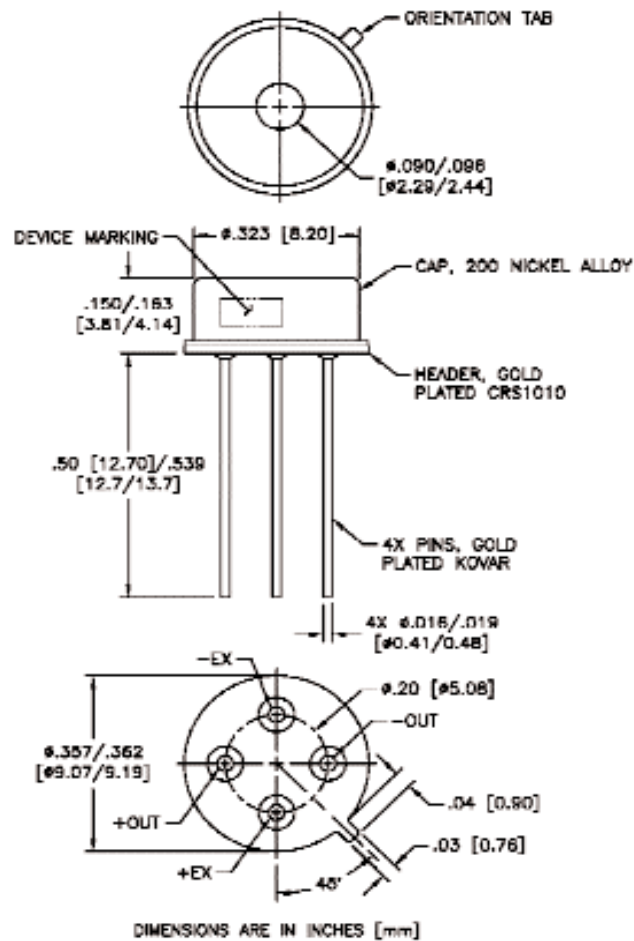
Dimensões do sensor de pressão MD-50-100mA [Extraído de (Datasheet Sensor MD-50-mA)].
